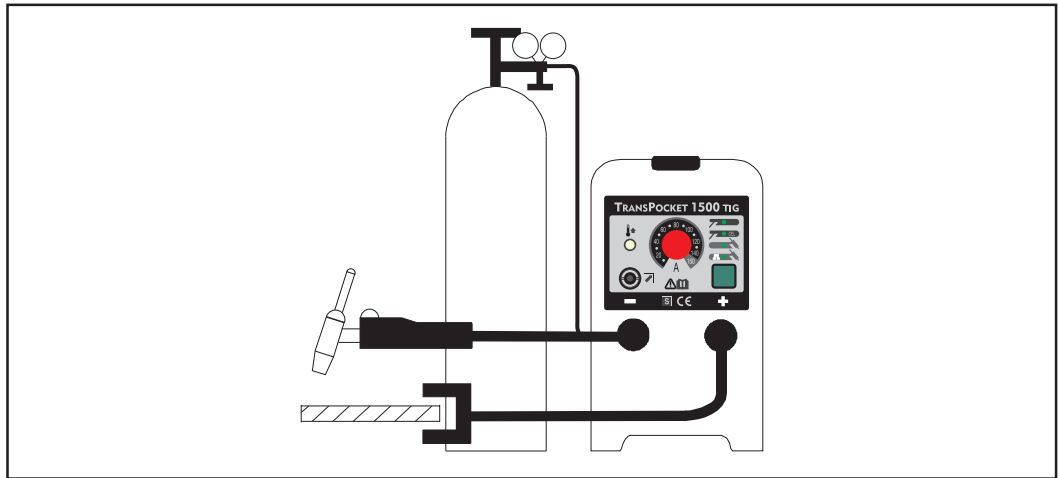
TP 1500 équipé pour le soudage TIG
